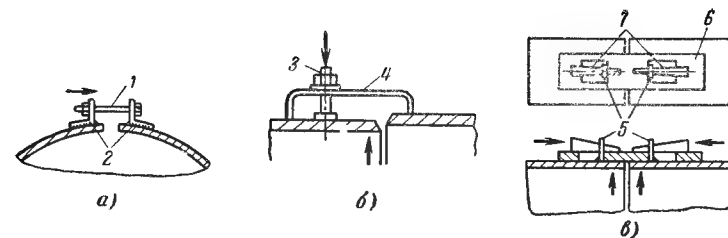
Натяжные приспособления для сборки обечайки под сварку.
